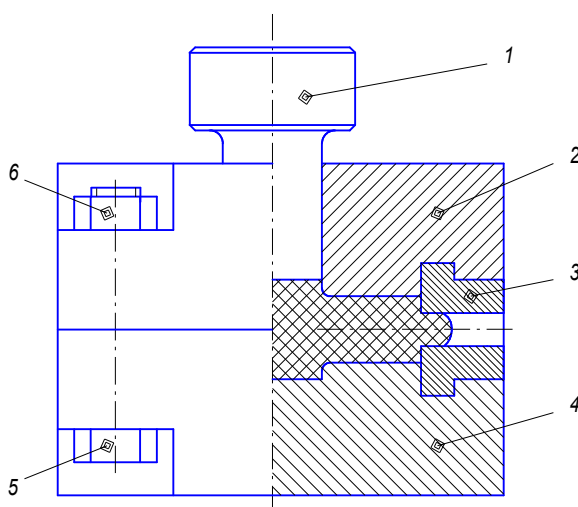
Лабораторный штамп с горизонтальным разъемом матрицы для штамповки поковок крестовины:
